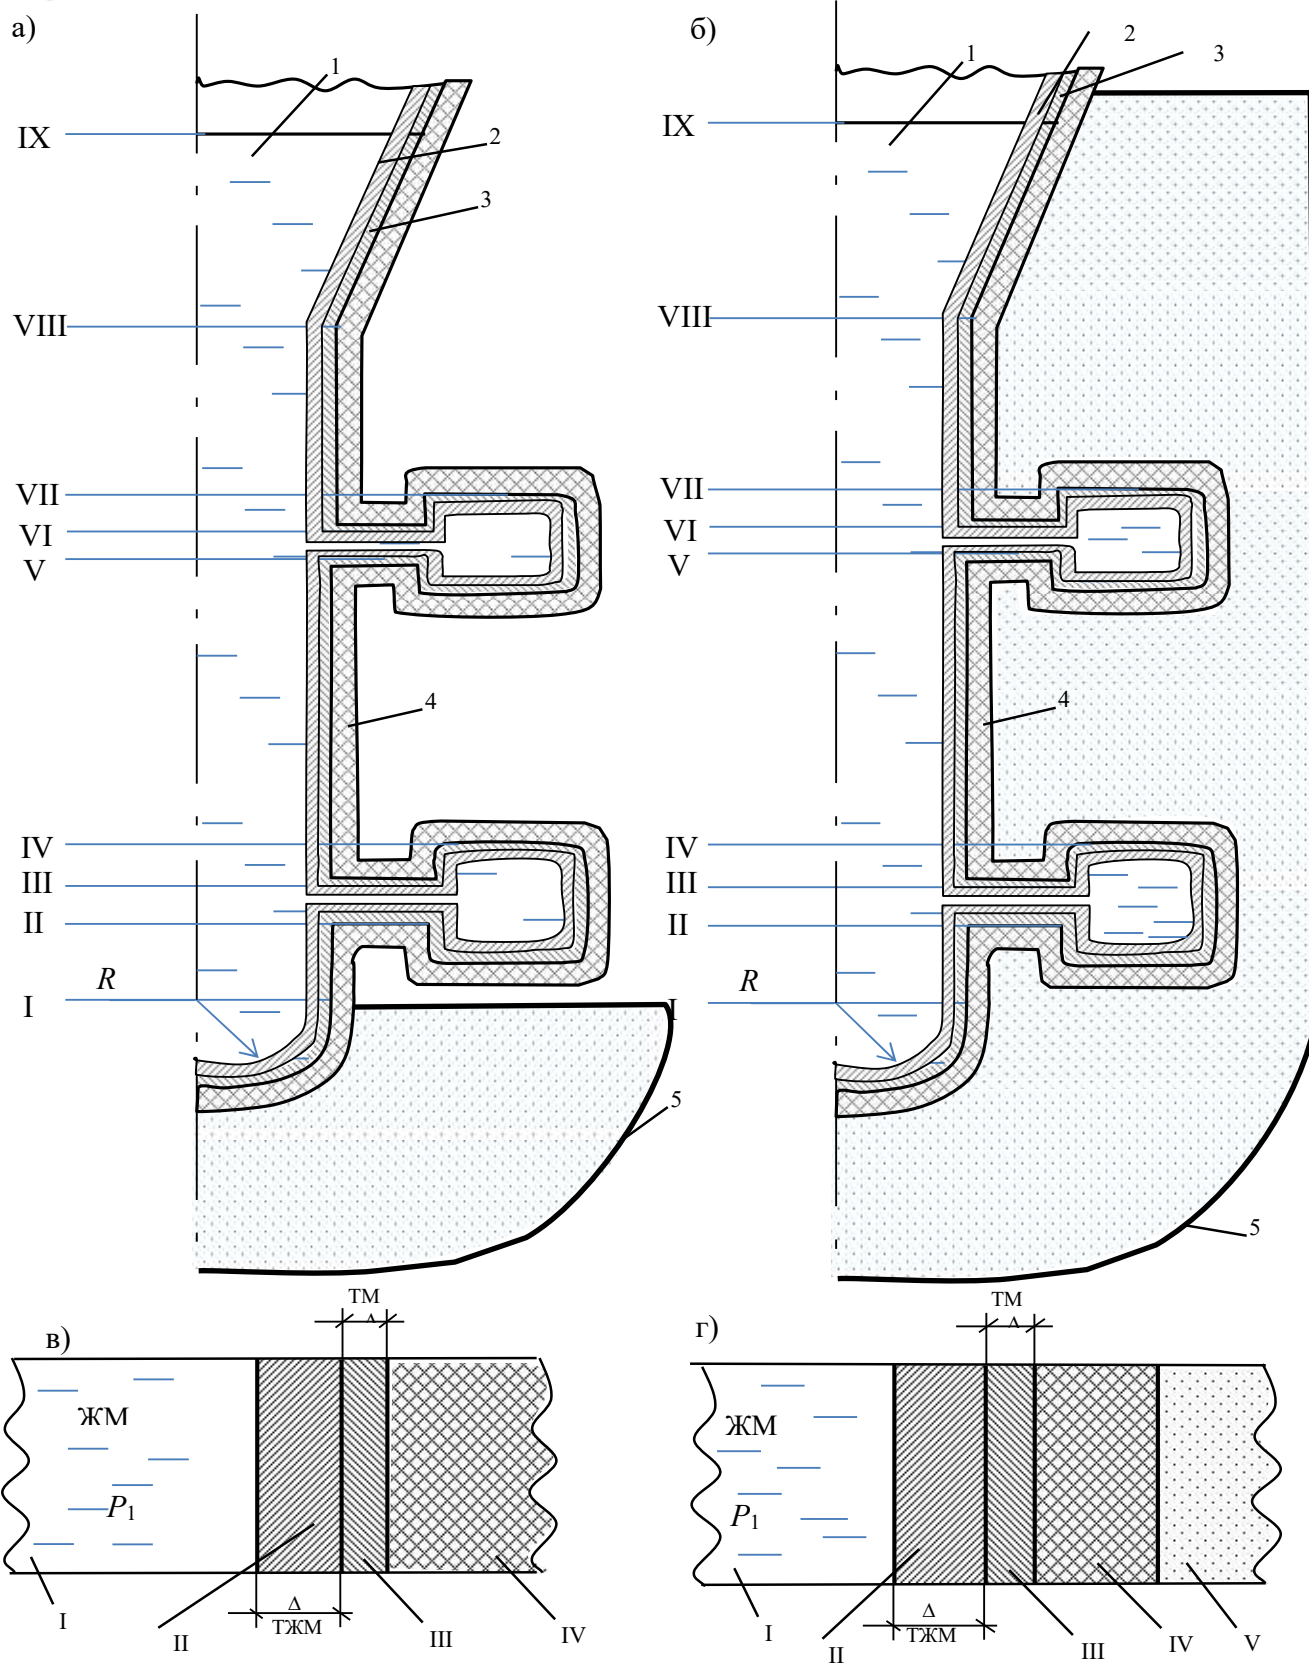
Схема охлаждения и затвердевания отливок: а – истинно ОФ; б – в опорном наполнителе: I...IX – контрольные уровни заливки по высоте ОФ; 1 – жидкий металл; 2 – твердожидкий слой металла; 3 – твердый слой металла; 4 – ОФ; 5 – поддон с ОН; в – расчетная схема моделирования НДС ОФ с указанием областей системы: I – жидкий металл; II – твердожидкий металл, III – твердый металл; IV – ОФ; г – расчетная схема моделирования НДС ОФ с указанием областей системы: I – жидкий металл; II – твердожидкий металл, III – твердый металл; IV – ОФ; V – ОН
